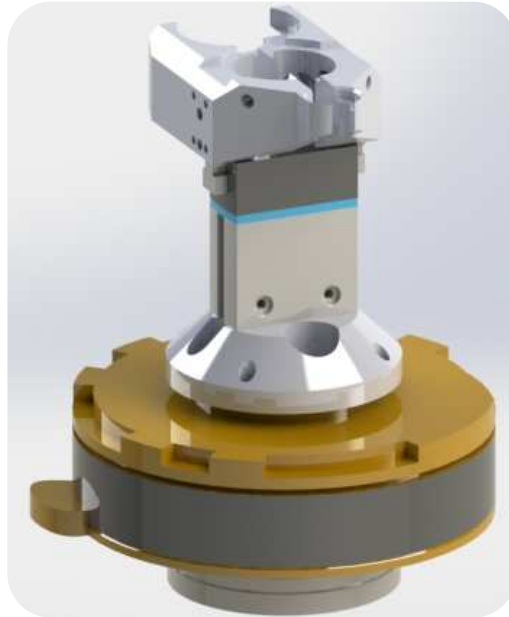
vista isomètrica de l'assemblatge del sensor de força i la pinça
